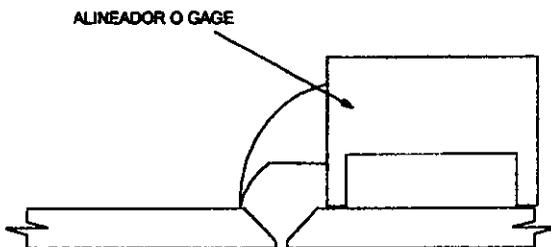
Croquis mostrando la Alineación de 2 secciones mediante un Gage o Escantillón de Soldadura
